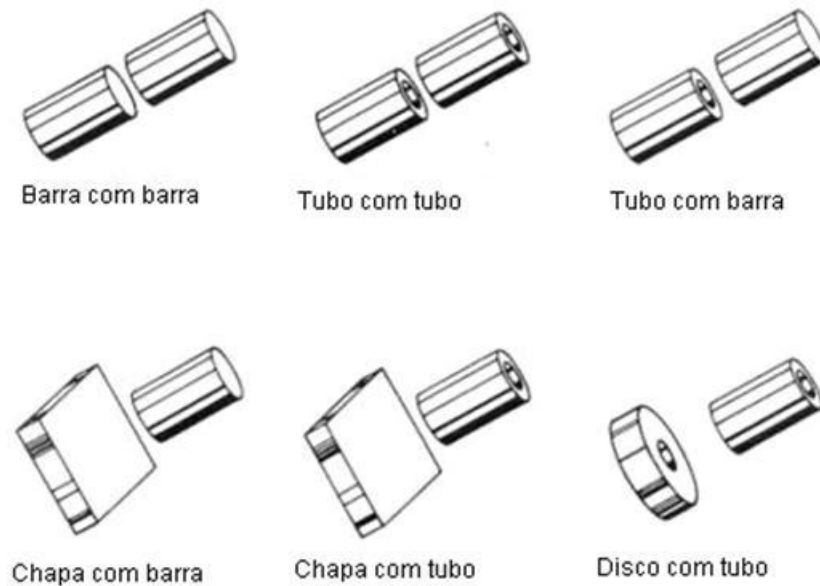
Geometrias típicas das peças que podem ser soldadas por fricção
